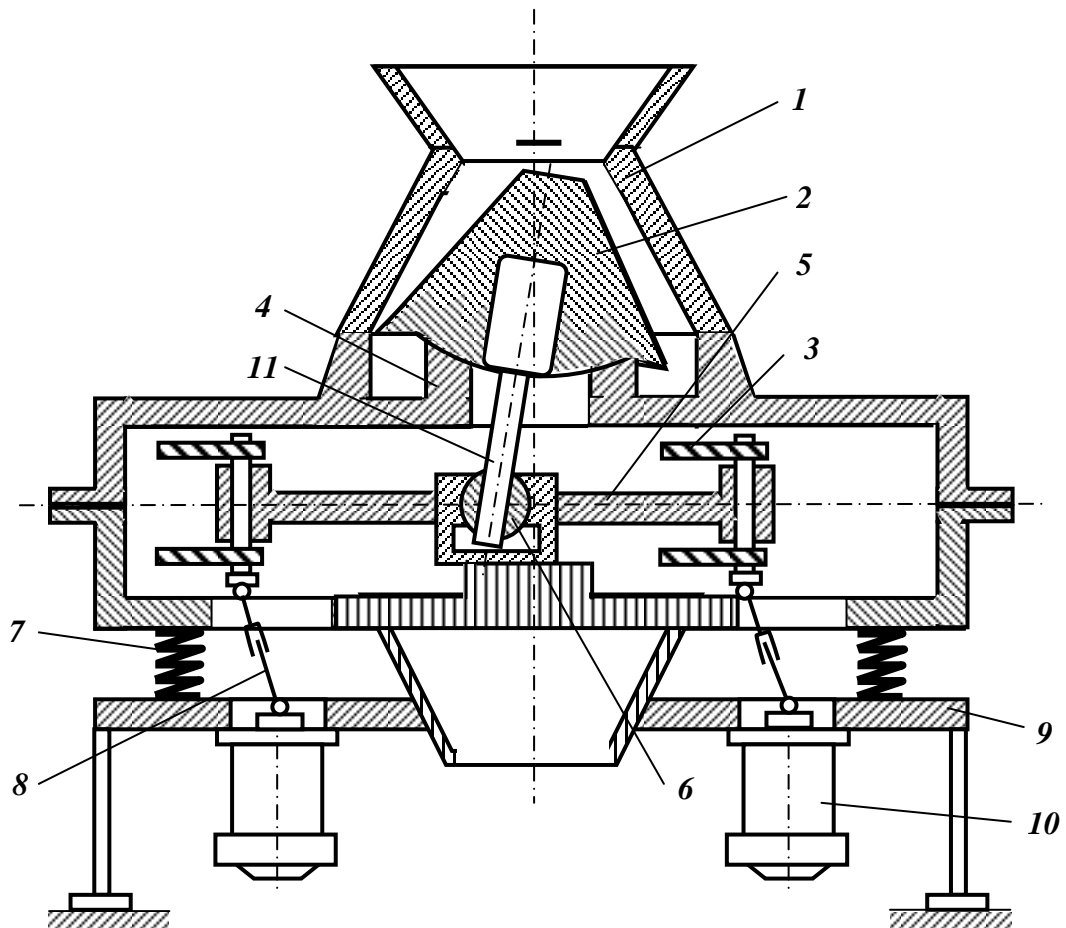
Схема конусної інерційної дробарки типу КІД.
